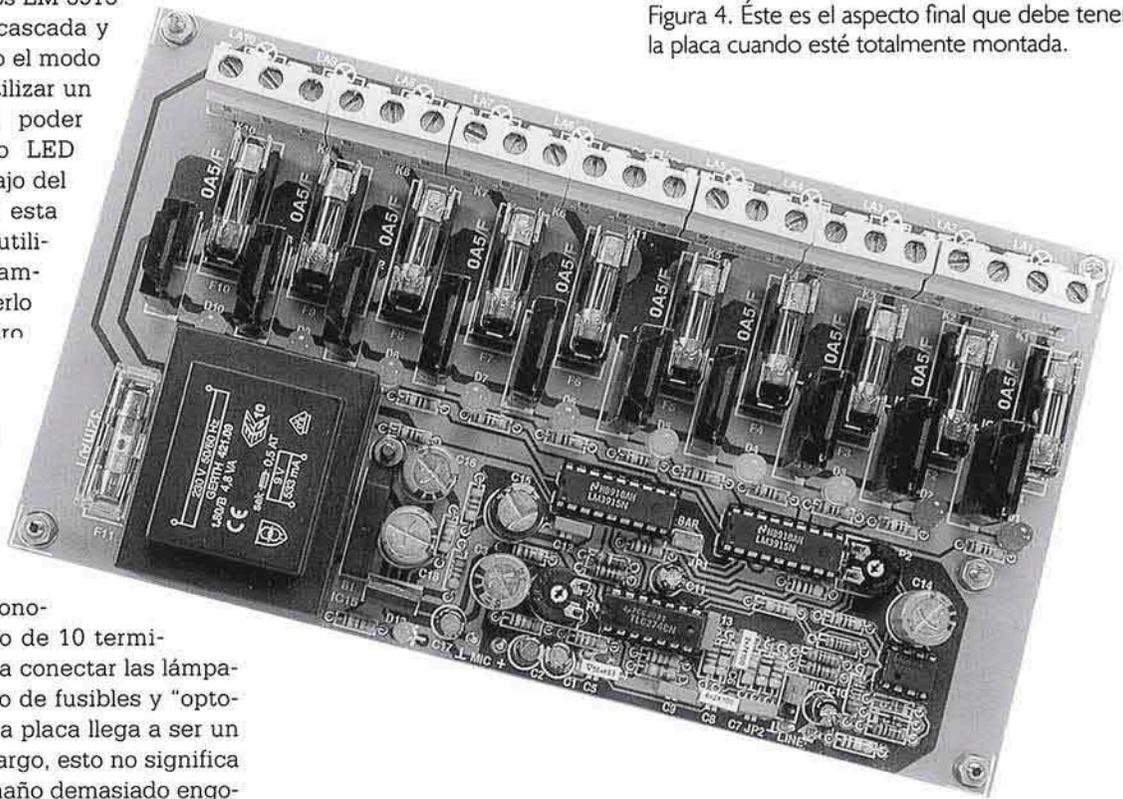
Éste es el aspecto final que debe tener la placa cuando esté totalmente montada.
